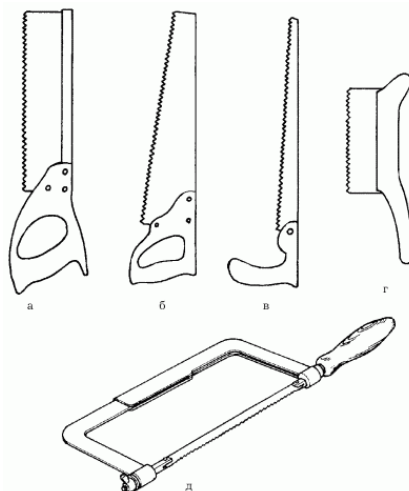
Виды ножовок: а – ножовка с обушком; б – ножовка поперечная широкая; в – ножовка узкая; г – ножовка-наградка; д – ножовка по металлу.
